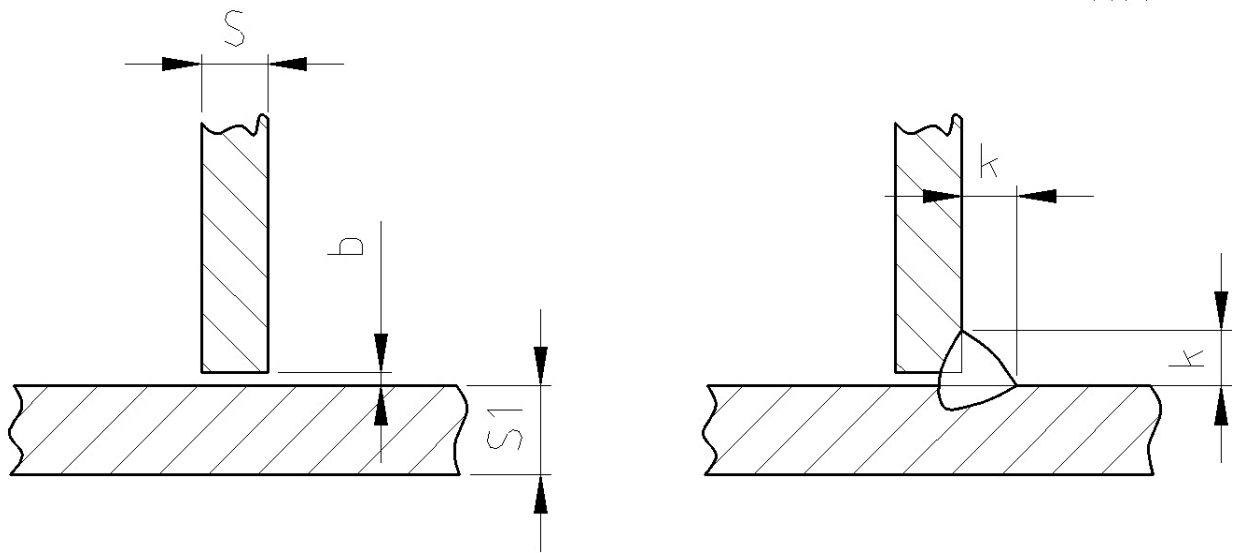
Эскиз сварного соединения II
